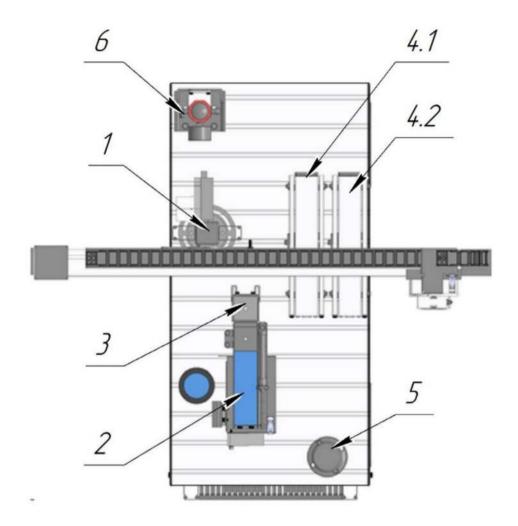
Конструкция мехатронной станции (вид сверху):
